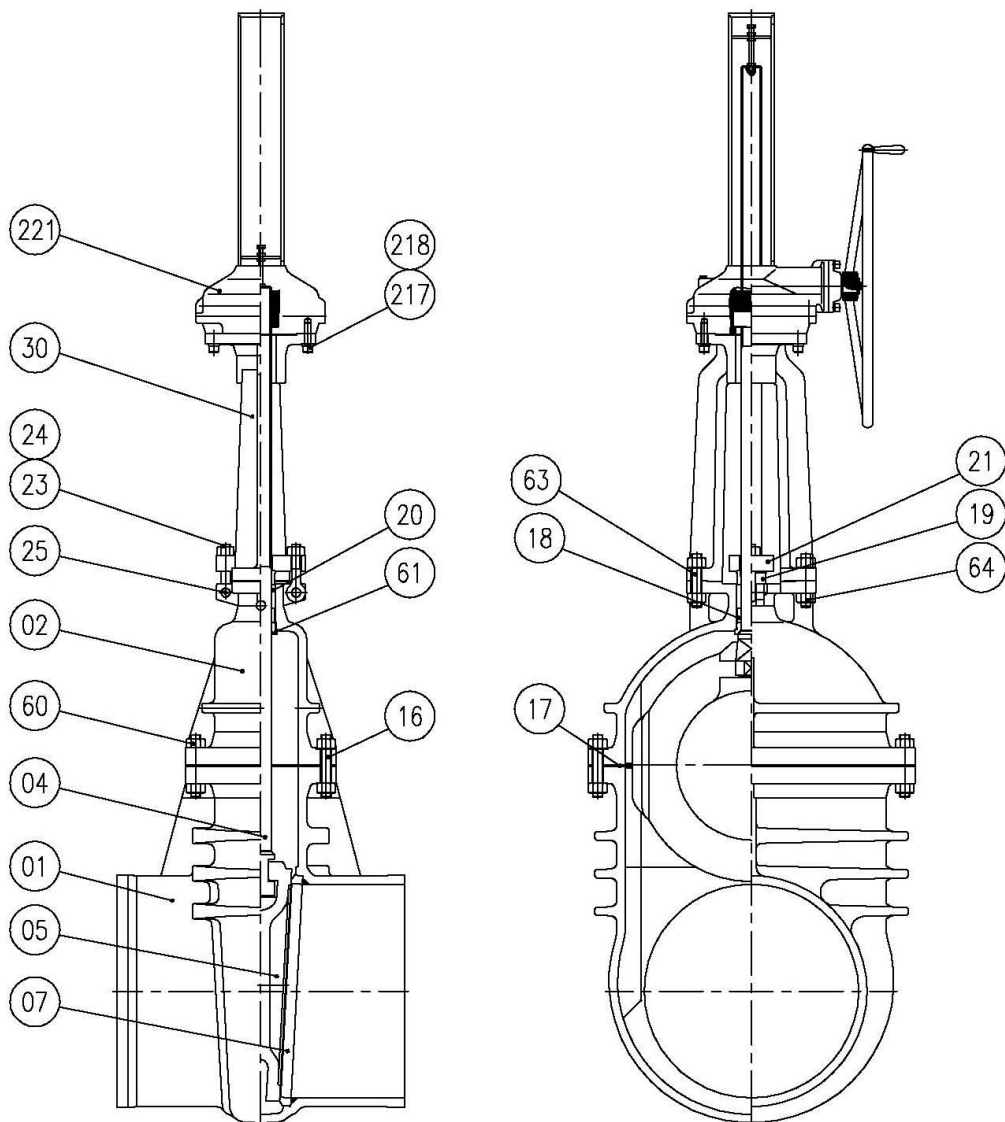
BOLTED BONNET & FLEXIBLE WEDGE GATE VALVE
